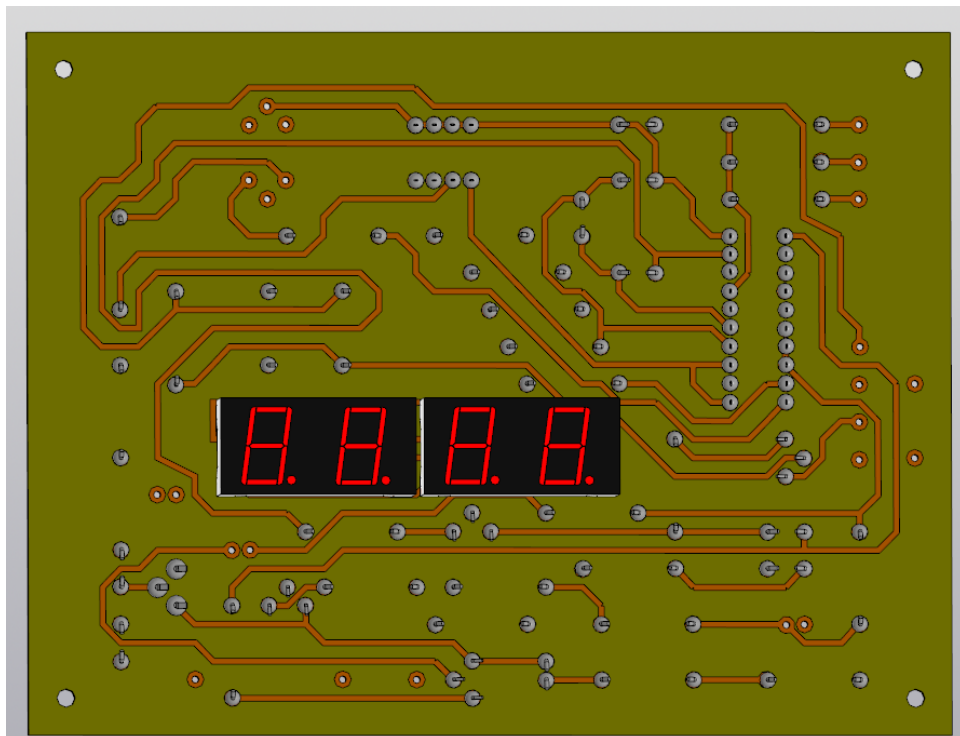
D вигляд плати друкованої з сторони пайки
